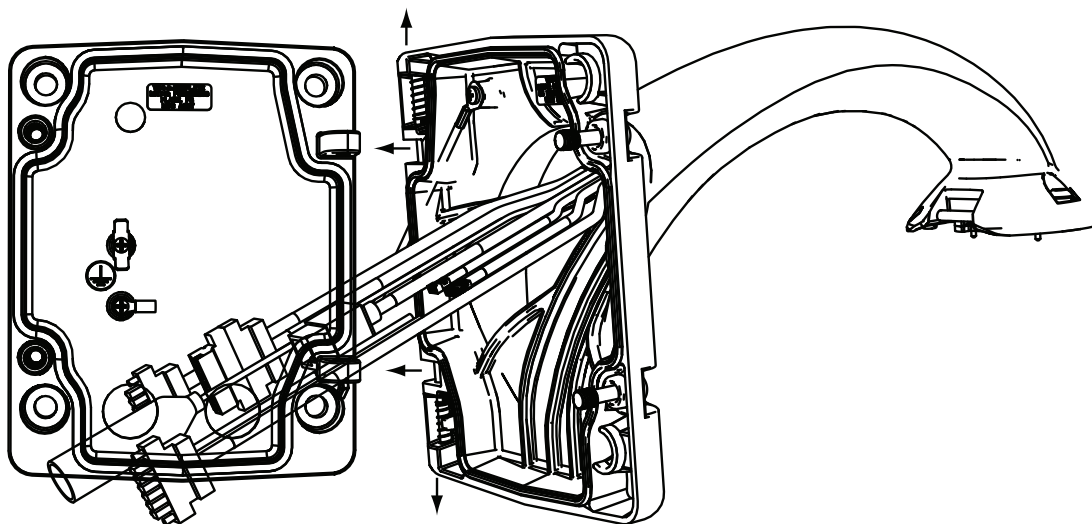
Conexión del brazo de pared a la placa de montaje
